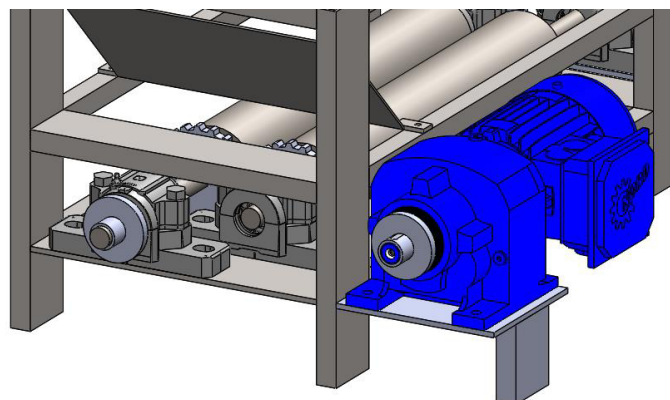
Apoio do motorreductor e representação das rodas-dentadas que conduzem a corrente de transmissão
